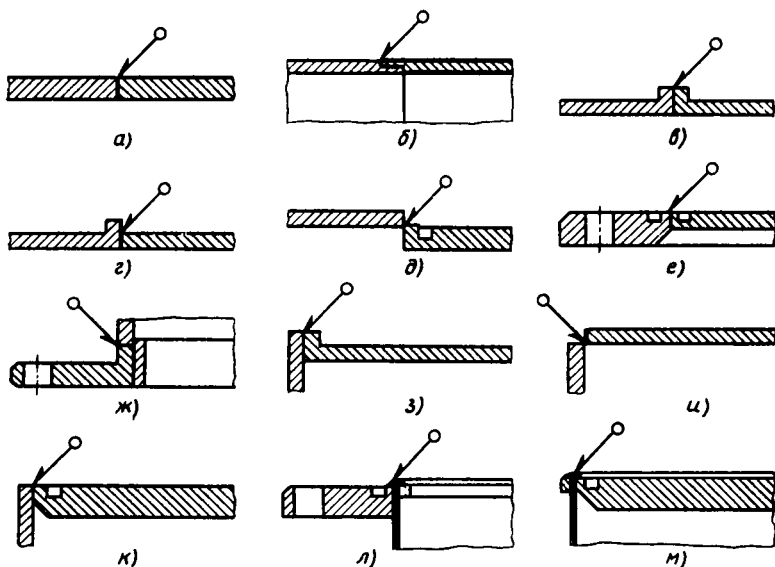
Примеры конструкций вакуумных сварных соединений:
